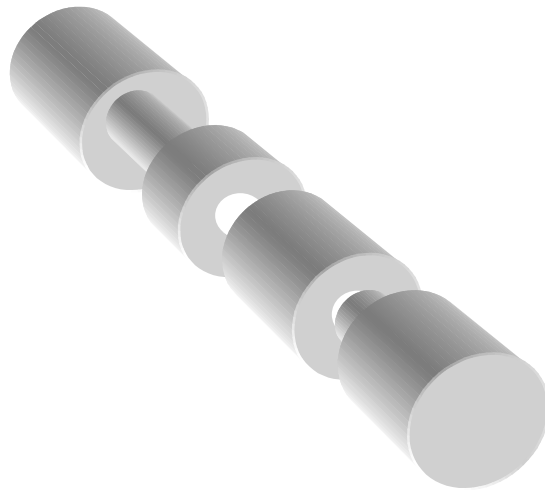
Molde para elaborar por presión las pastillas que luego se van a someter al ensayo de cizalla.
